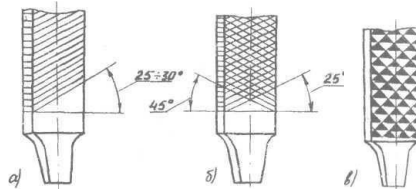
Виды насечек напильников: а) одинарная, б) двойная, в) рашпильная.
